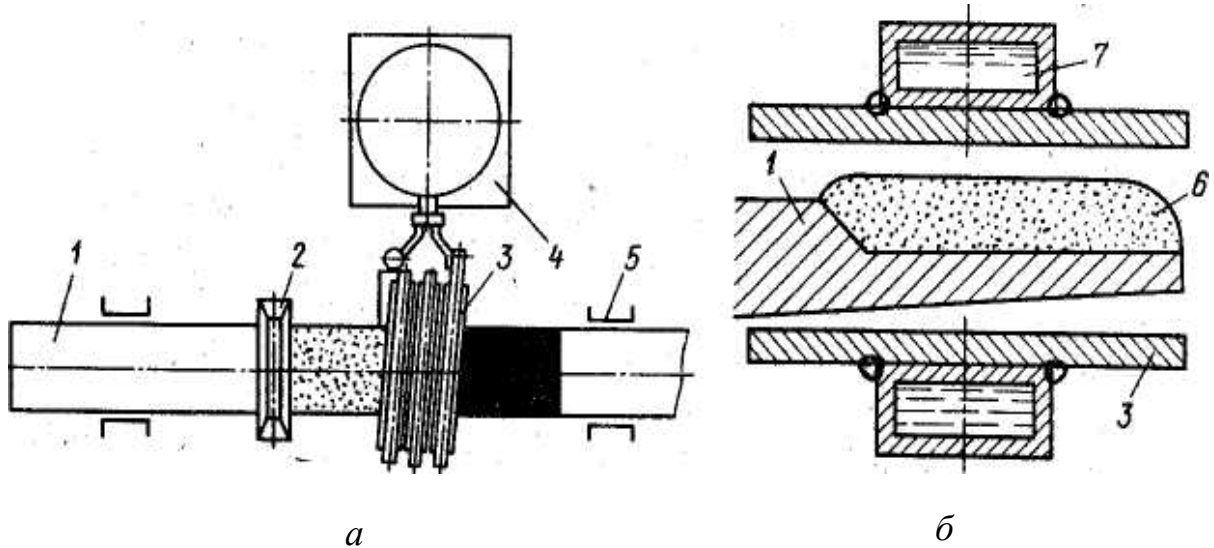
Схеми індукційного (високочастотного) наплавлення: *а* — циліндричних; *б* — плоских деталей; 1 — деталь, що наплавляється; 2 — дозатор; 3 — індуктор; 4 — трансформатор; 5 — направляючі; 6 — шар шихти (присадного матеріалу); 7 — вода для охолодження індуктора
